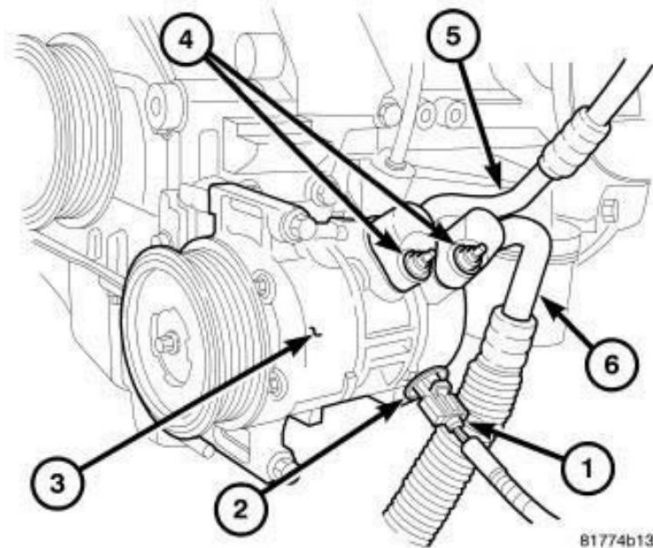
Líneas de refrigerante del compresor del aire acondicionado
